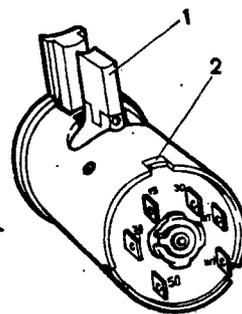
Вид на контактную часть выключателя зажигания: 1 - запорный стержень; 2 - широкий выступ контактной части
